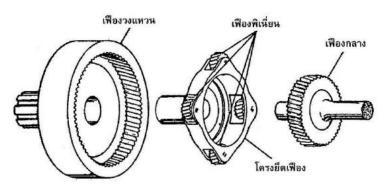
ชุดเฟืองแพลนเนตตารี่ (Planetary Gear) [8]
